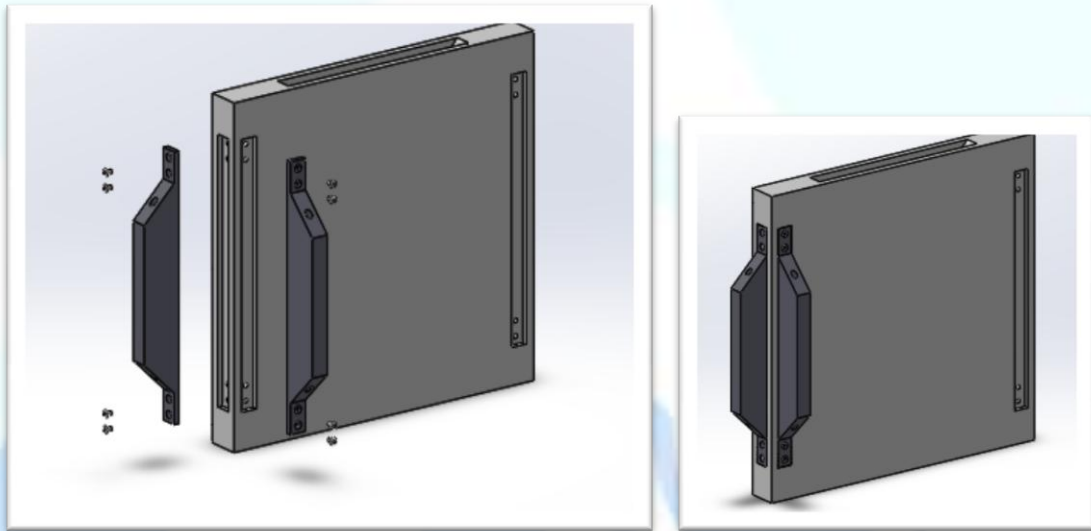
explosionado panel con machos (izquierda), panel con machos (derecha)
